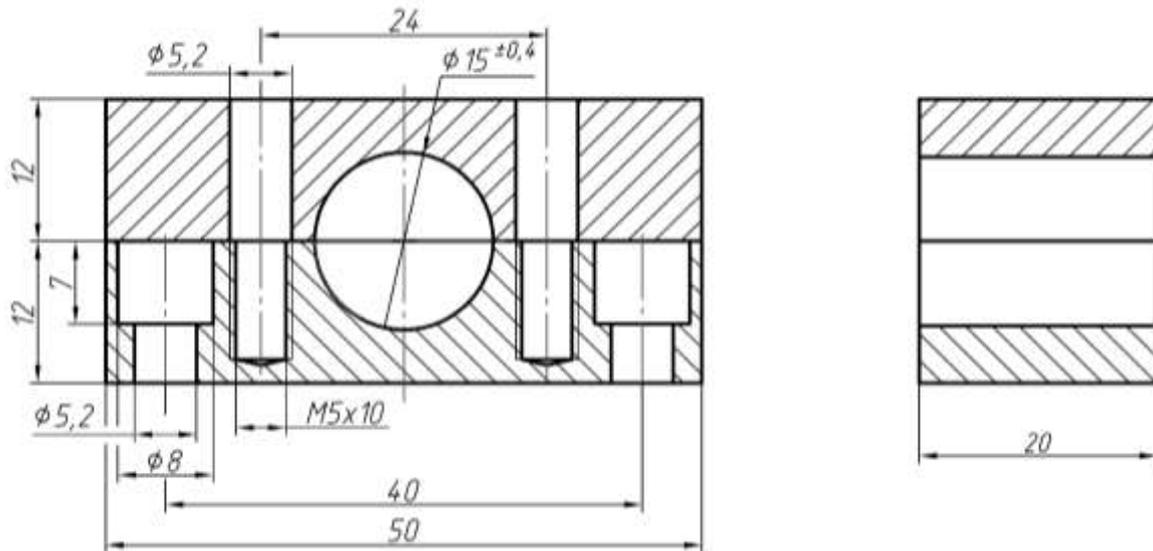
Чертеж «хомута» - фиксатора крепления «1-й точки» кабеля «ЦДВ»
